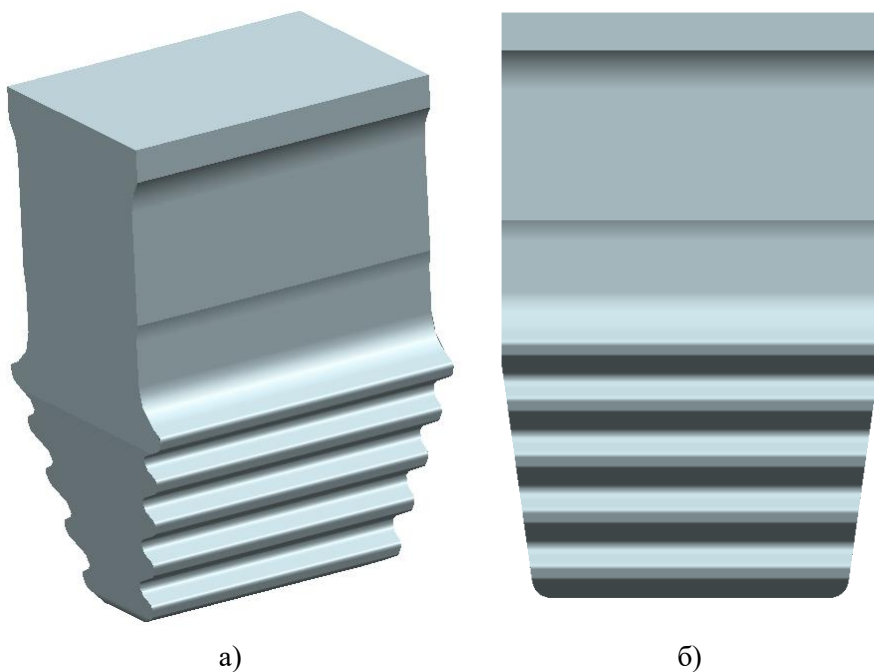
CAD 3D-модель удлиненной ножки хвостовика елочного типа: а) изометрия, б) главный вид
